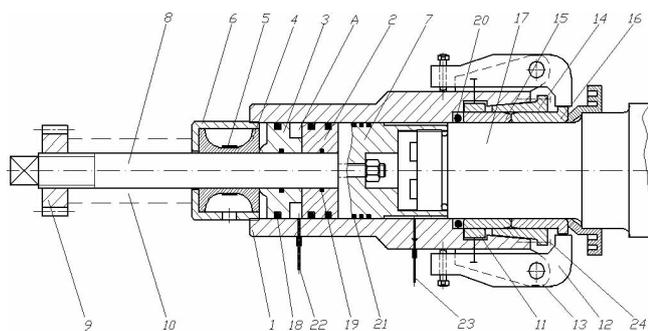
Устройство для контроля прочности на сдвиг и распрессовки колец подшипников колёсных пар
